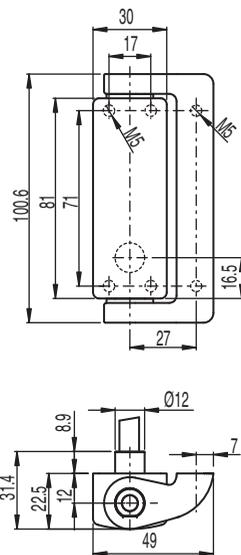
Dimensões do S400-M4-CB2PUR-W em mm
